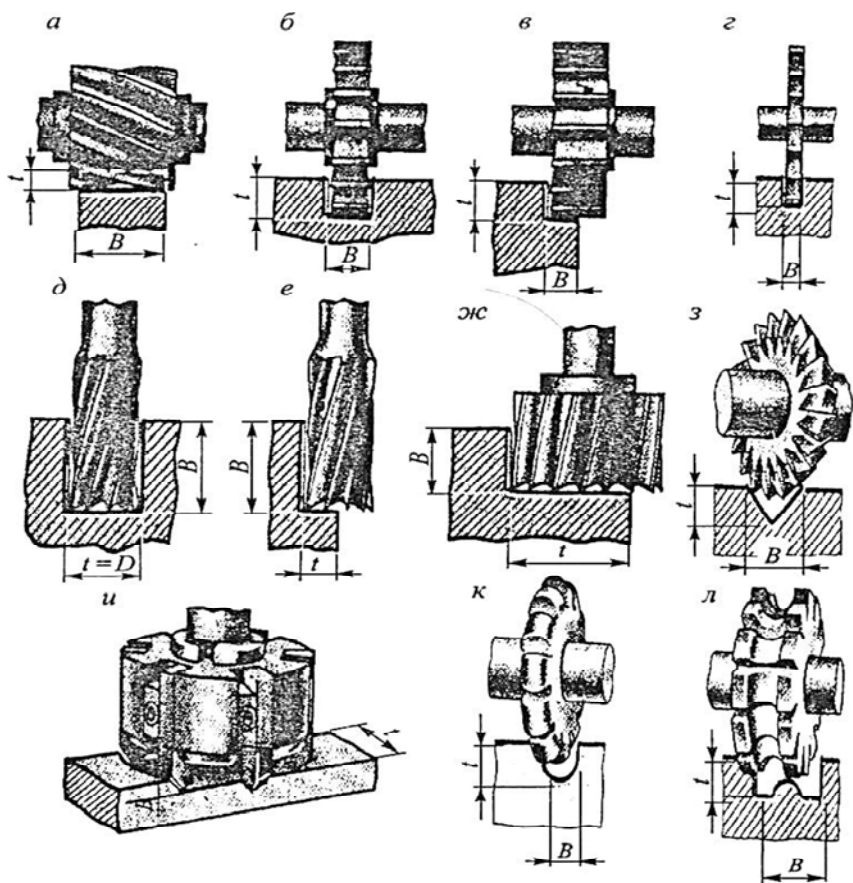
Ширина фрезерования B и глубина резания t при обработке деталей машин на фрезерных станках
